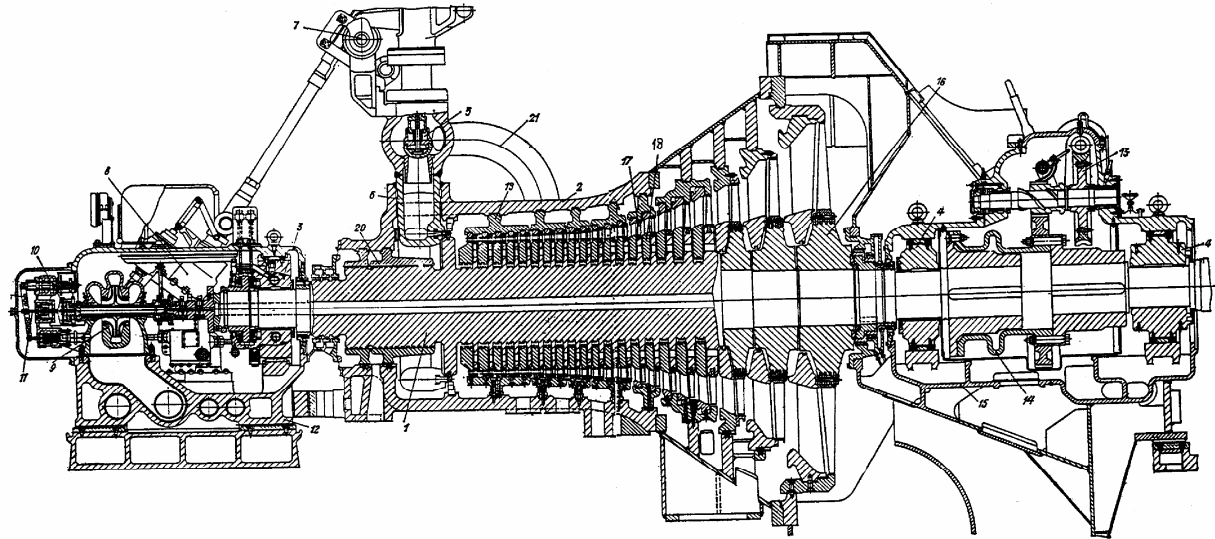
Продольный разрез турбины К-50-90: 1 – ротор турбины; 2 – корпус турбины; 3 – опорно-упорный подшипник; 4 – опорный подшипник; 5 – регулирующий лапан; 6 – сопловая коробка; 7 – кулачковый вал; 8 – сервомотор; 9 – главный масляный насос; 10 – регулятор скорости; 11 – следящий золотник; 12 – картер переднего подшипника; 13 – валоповоротное устройство; 14 – соединительная муфта; 15 – выхлопной патрубок турбины; 16 – насадные диски; 17 – рабочие лопатки; 18 – диафрагмы; 19 – обоймы диафрагм; 20 – обоймы концевой уплотнения; 21 – перепускная труба (от стопорного к регулируемому клапану).
